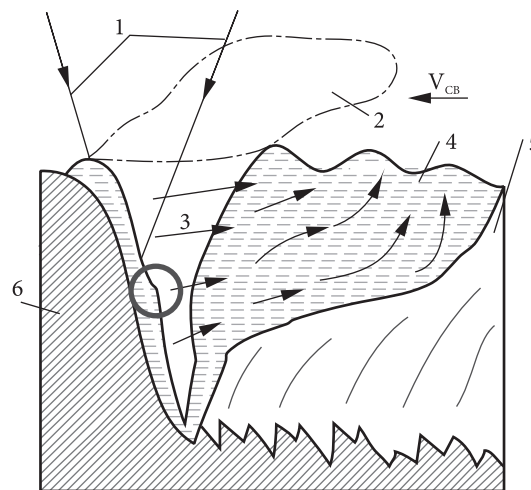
Схема сварочной ванны при лазерной сварке: 1 – лазерный луч; 2 – плазменный факел; 3 – парогазовый канал; 4 – хвостовая часть ванны; 5 – металл шва; 6 – свариваемый металл; V_{CB} – направление сварки
